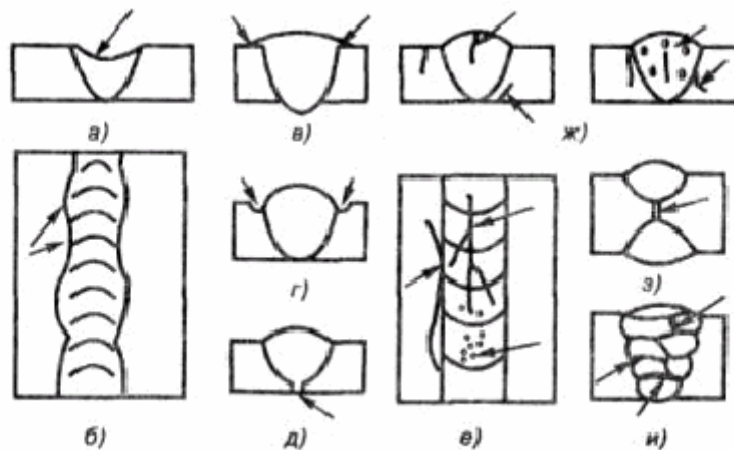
Виды дефектов сварных швов: а – ослабление шва, б – неравномерность ширины, в – наплыв; г – подрез, д – непровар, е – трещины и поры, ж – внутренние трещины и поры, з – внутренний непровар, шлаковые включения.
